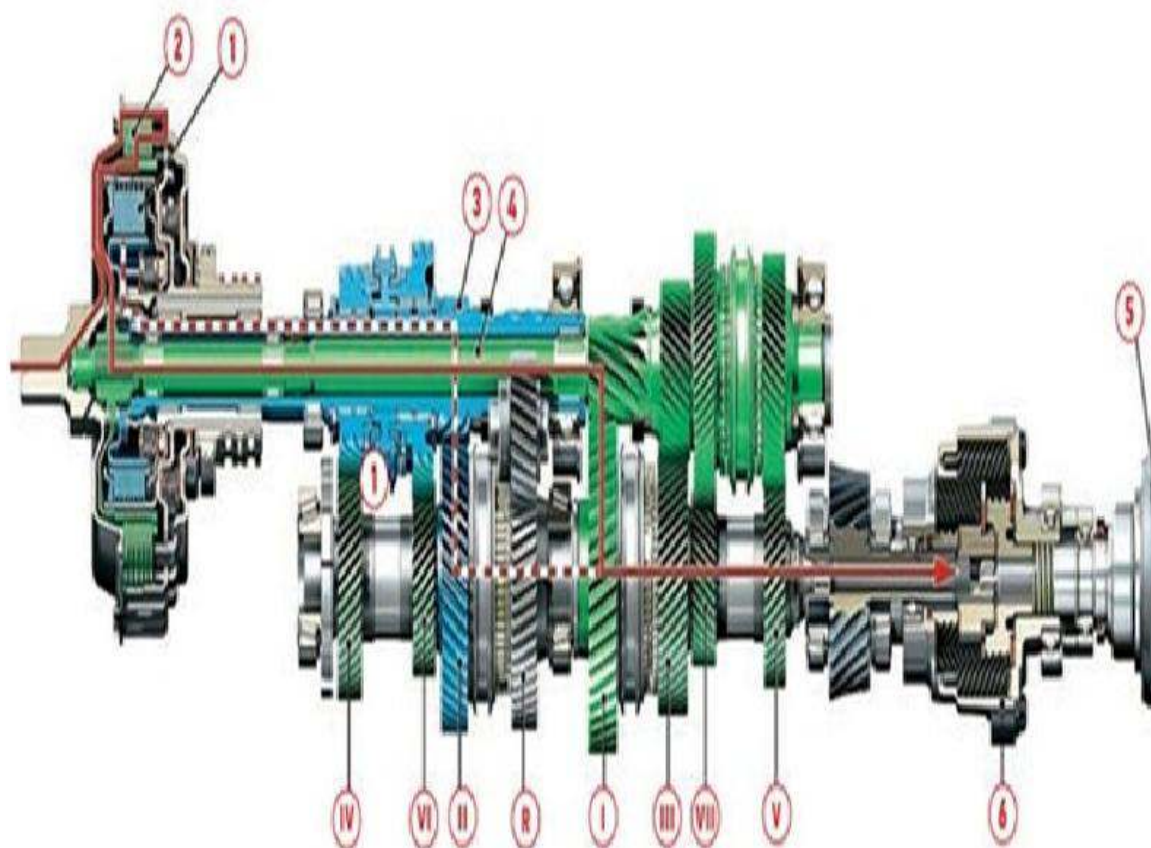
Схема трехвальной коробки передач с двойным сцеплением:
